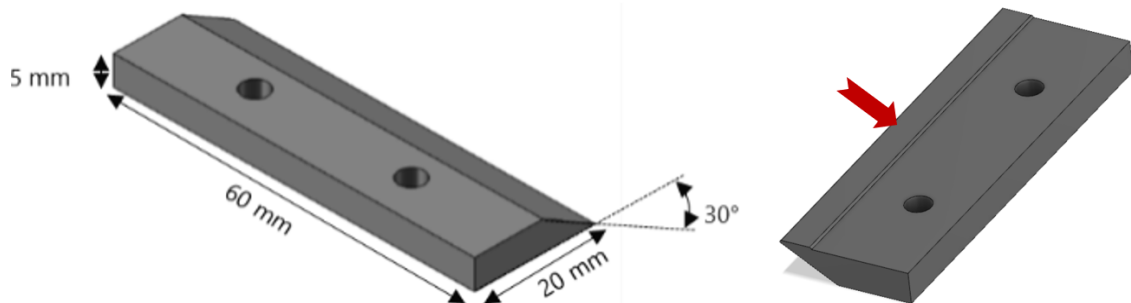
Géométrie des couteaux réalisés pour les essais de coupe sur le banc TEEMO.
